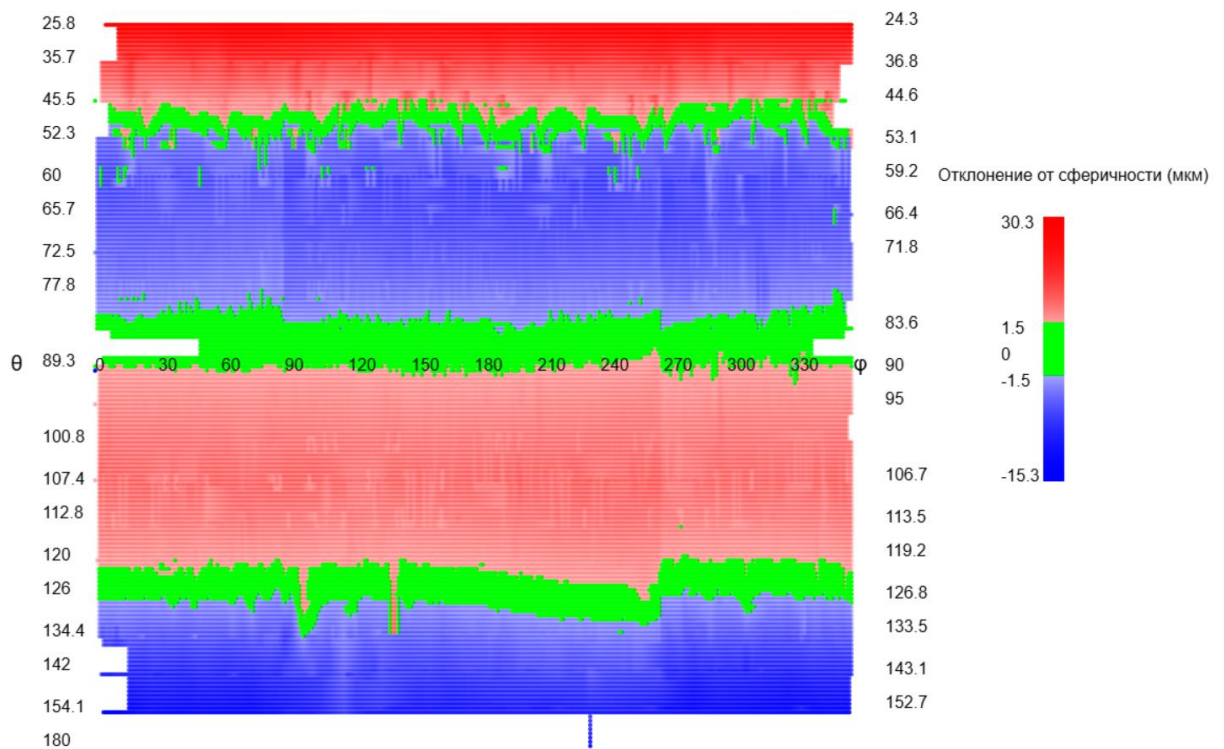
Развертка сферической поверхности шарового пальца №4 после притирки
